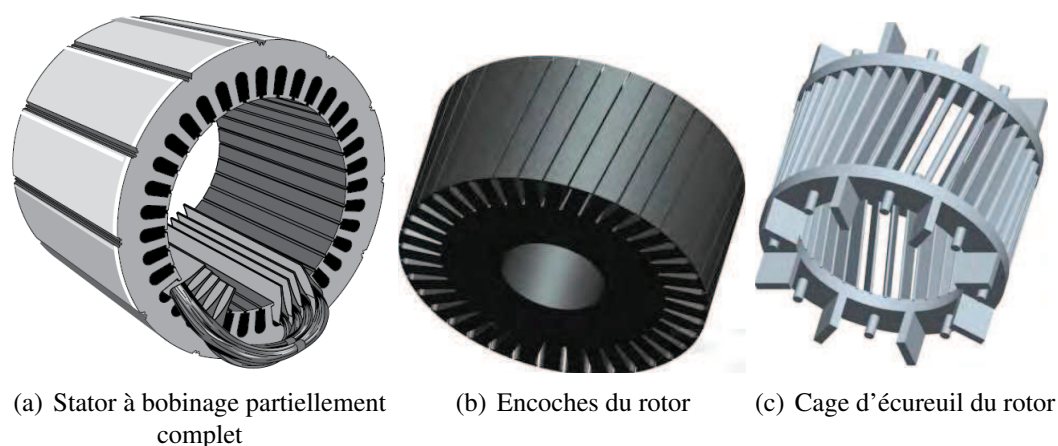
Architecture en 3D de la machine à induction à cage d'écureuil
